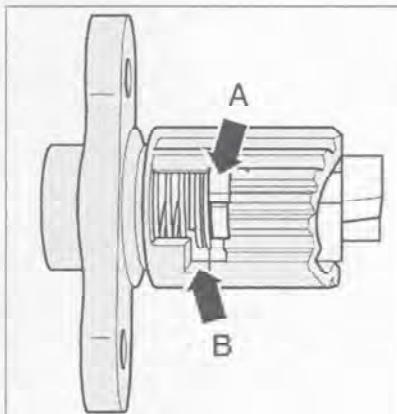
Перед установкой механизма проследите, чтобы выступ втулки (стрелка А) располагался в противоположной стороне от канавки корпуса (стрелка В).
